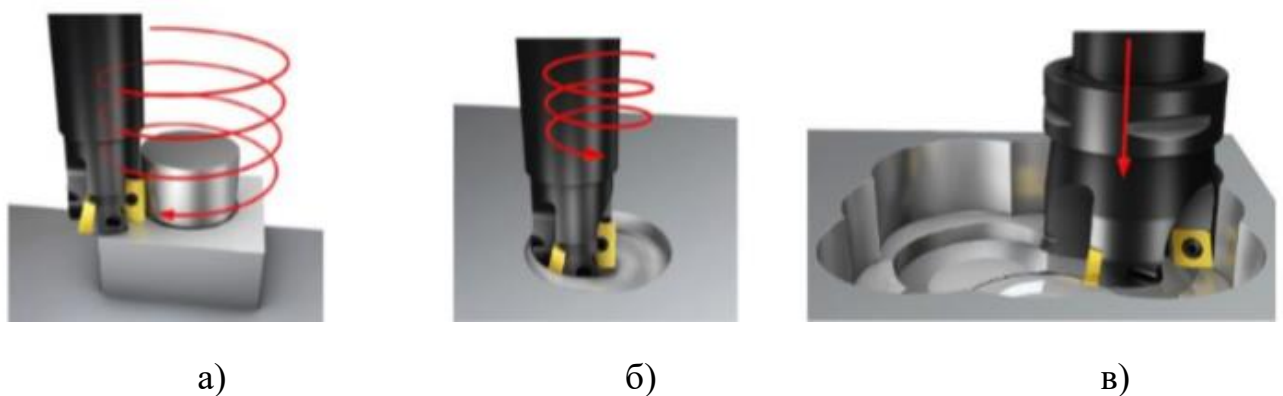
Кінематичні схеми ВШО на верстатах з ЧПК при фрезеруванні [5]
